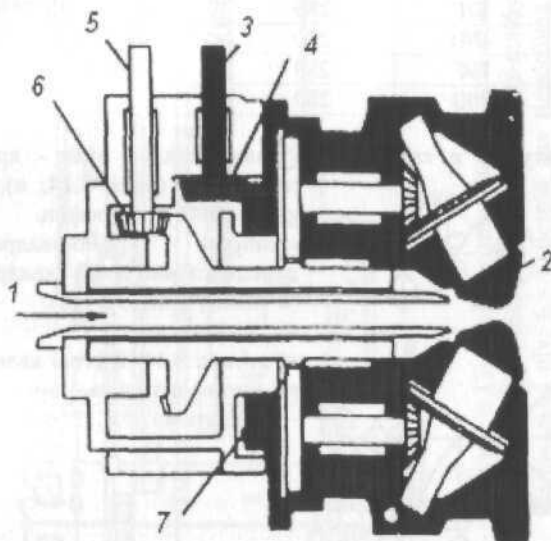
Косо-валковий планетарний стан: 1 - заготовка; 2 - валки; 3 - вал приводу обертання валків навколо заготовки; 4, 6 - конічні передачі; 5 - вал приводу обертання валків навколо своєї осі; 7 - циліндрична передача
